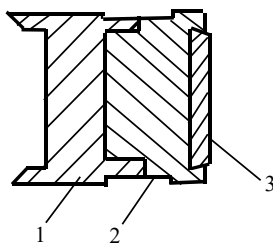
Продольный разрез комбинированного ударника: 1 — полиэтиленовый колпачок, 2 — башмак из поликарбонатной пластмассы; 3 — металлическая пластина-ударник
